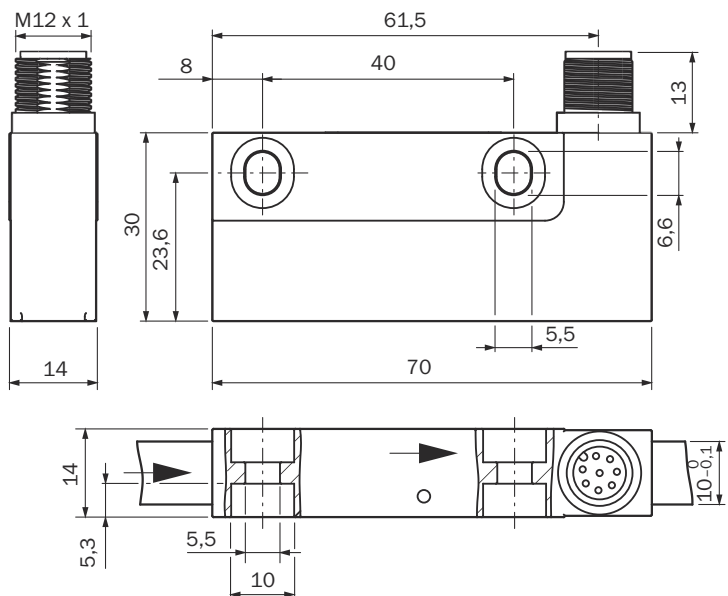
Maßzeichnung TTK70S mit Stecker M12 (alle Maße in mm)
